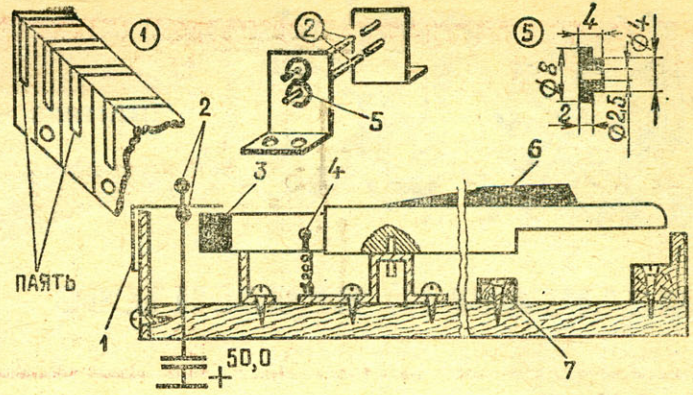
Устройство клавиатуры: 1 — контактная пластина, 2 — сборные шины, 3 — резиновый изолятор, 4 — пружина, 5 — изолирующая прокладка, 6 — клавиша, 7 — ограничитель хода клавиши.
